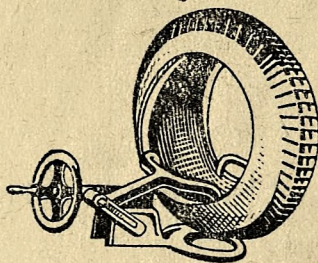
Укрепляемое на верстаке приспособление для разжимания бортов больших покрышек
